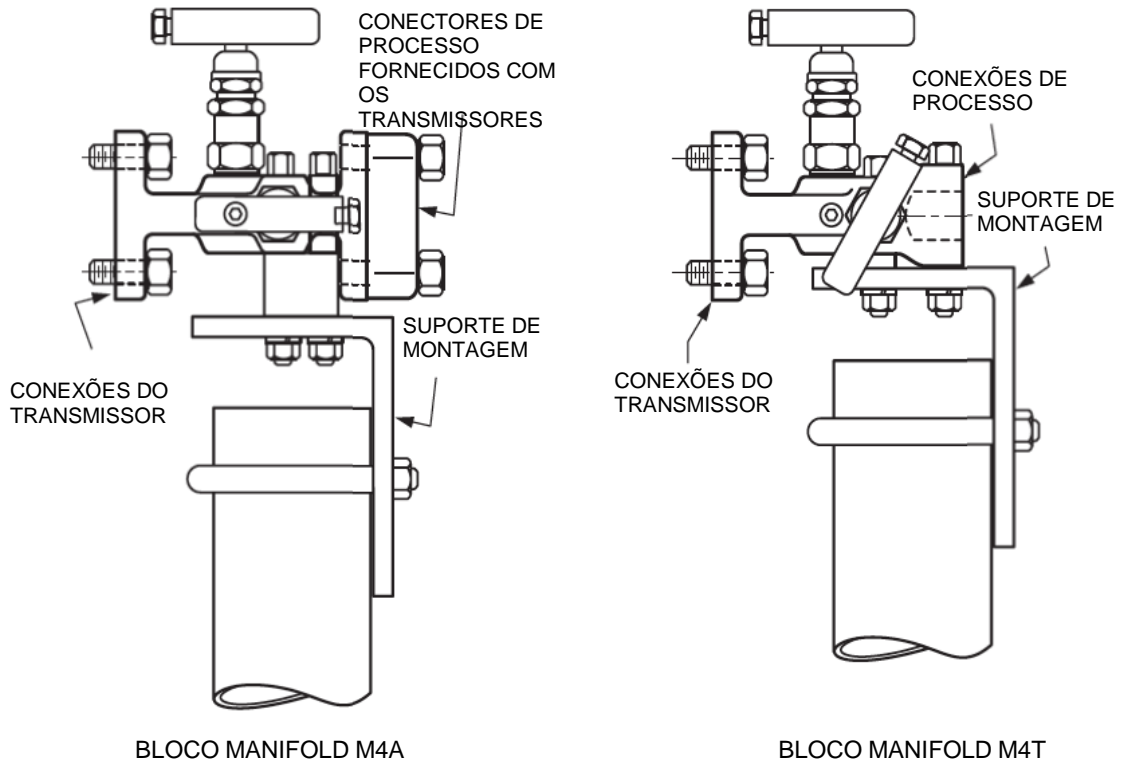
Montagem Típica dos Blocos de Manifold M4A e M4T com Suporte - AM
